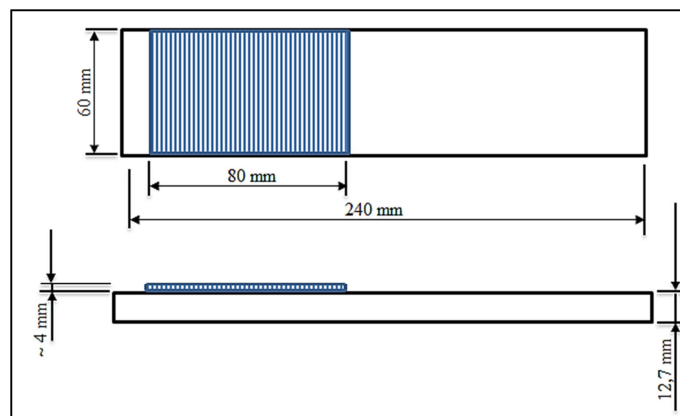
Dimensões da peça soldada pelo processo de soldagem de revestimento PTA com pó de Inconel 625, Nistelle 625.
